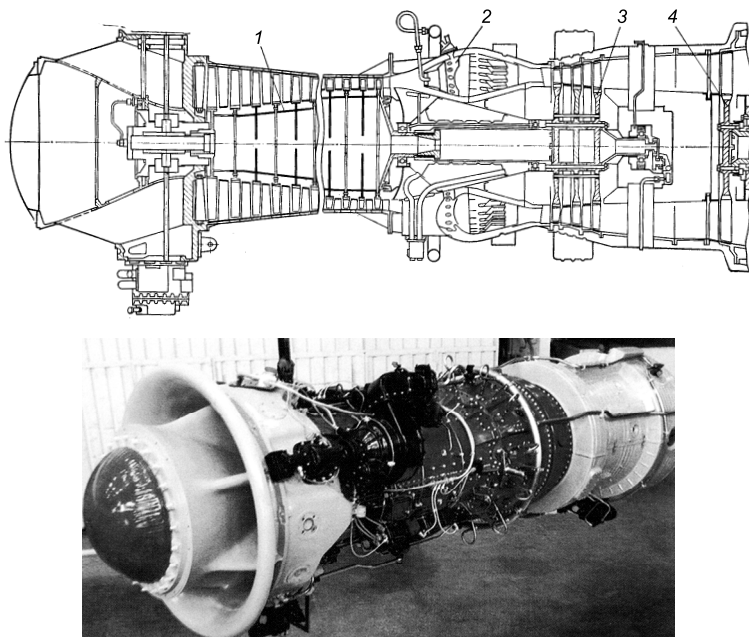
Конструктивная схема ГТУ НК-12СТ [5] и ее внешний вид (внизу).
